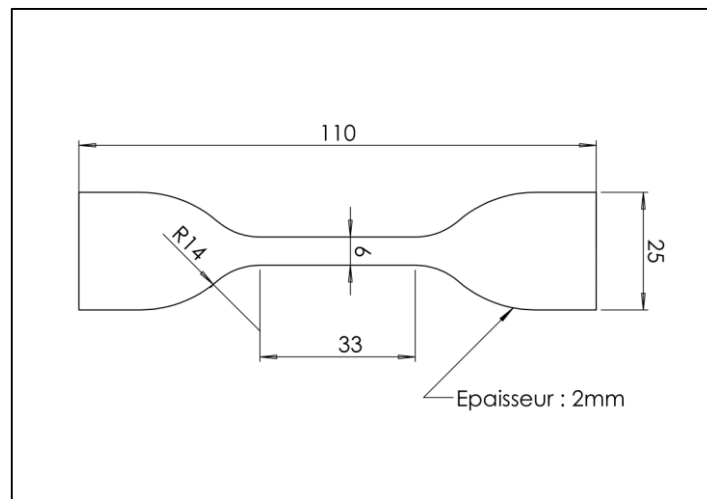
Les dimensions de l'éprouvette conforme a la Norme ASTM D412
